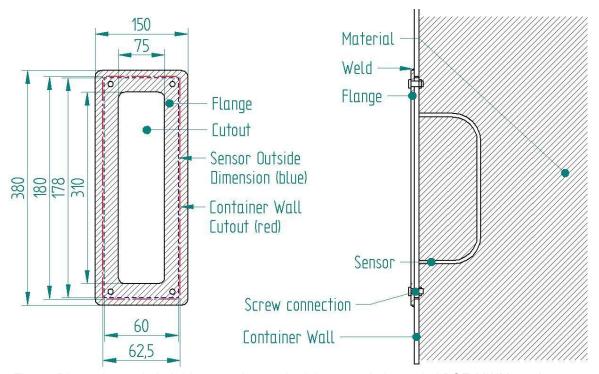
Dimensiones de la brida para el montaje del sensor de humedad PCE-MWM 240A
